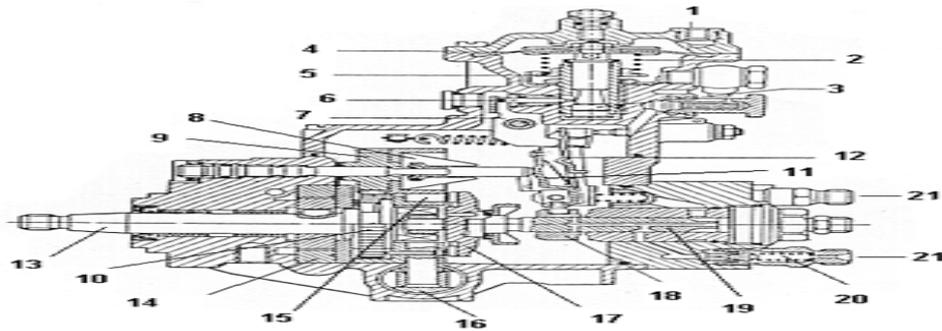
Despiece de la bomba Mecánica Radial Tipo VP 29
